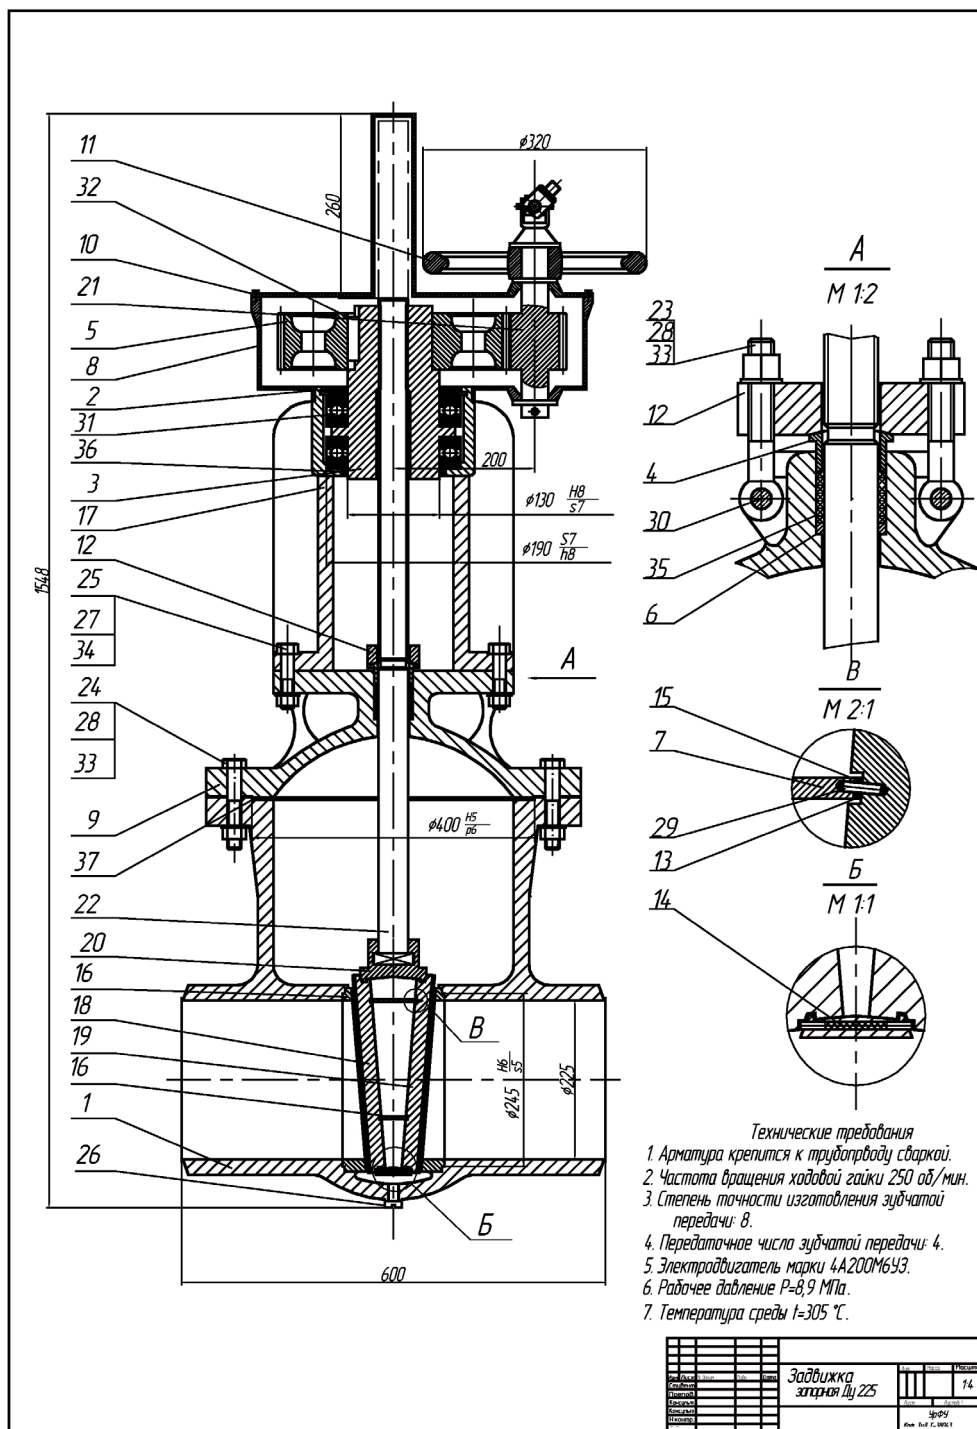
Задвижка запорная. Сборочный чертеж
